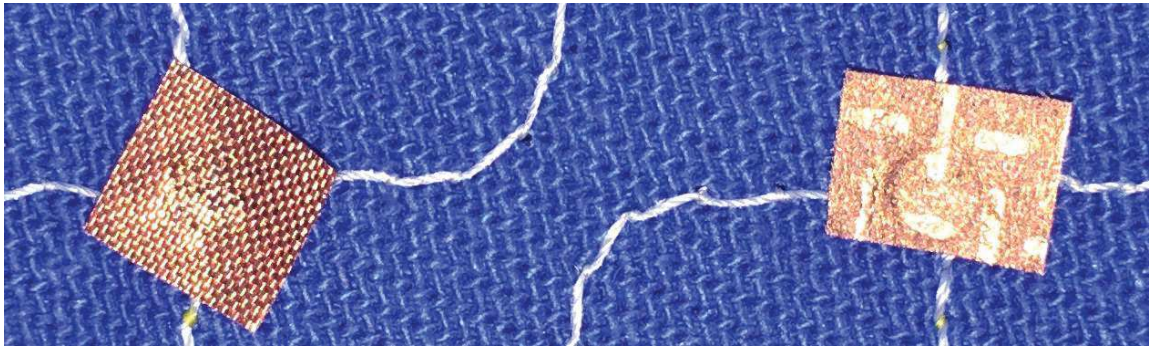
Kontaktování pomocí krimpovaných spojů
